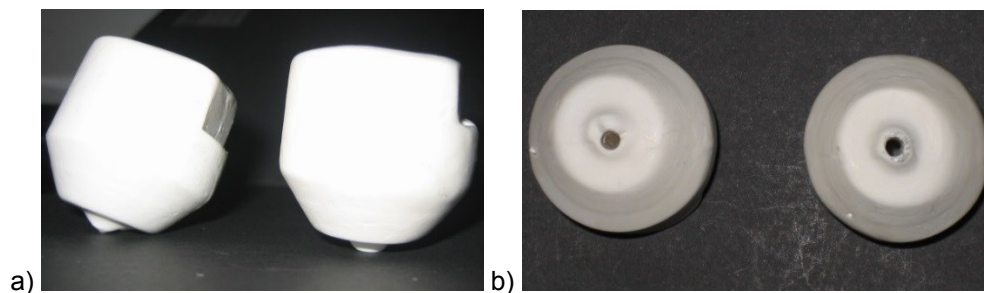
Fotos das ferramentas em alumina; a) Perfil, b) Vista de planta.
